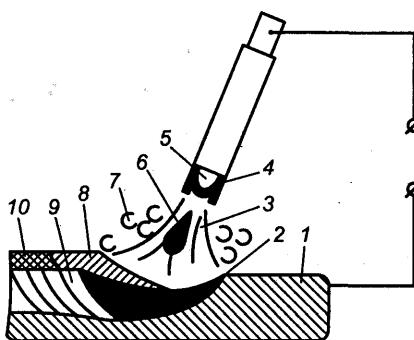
Схема ручной дуговой сварки покрытым электродом:
